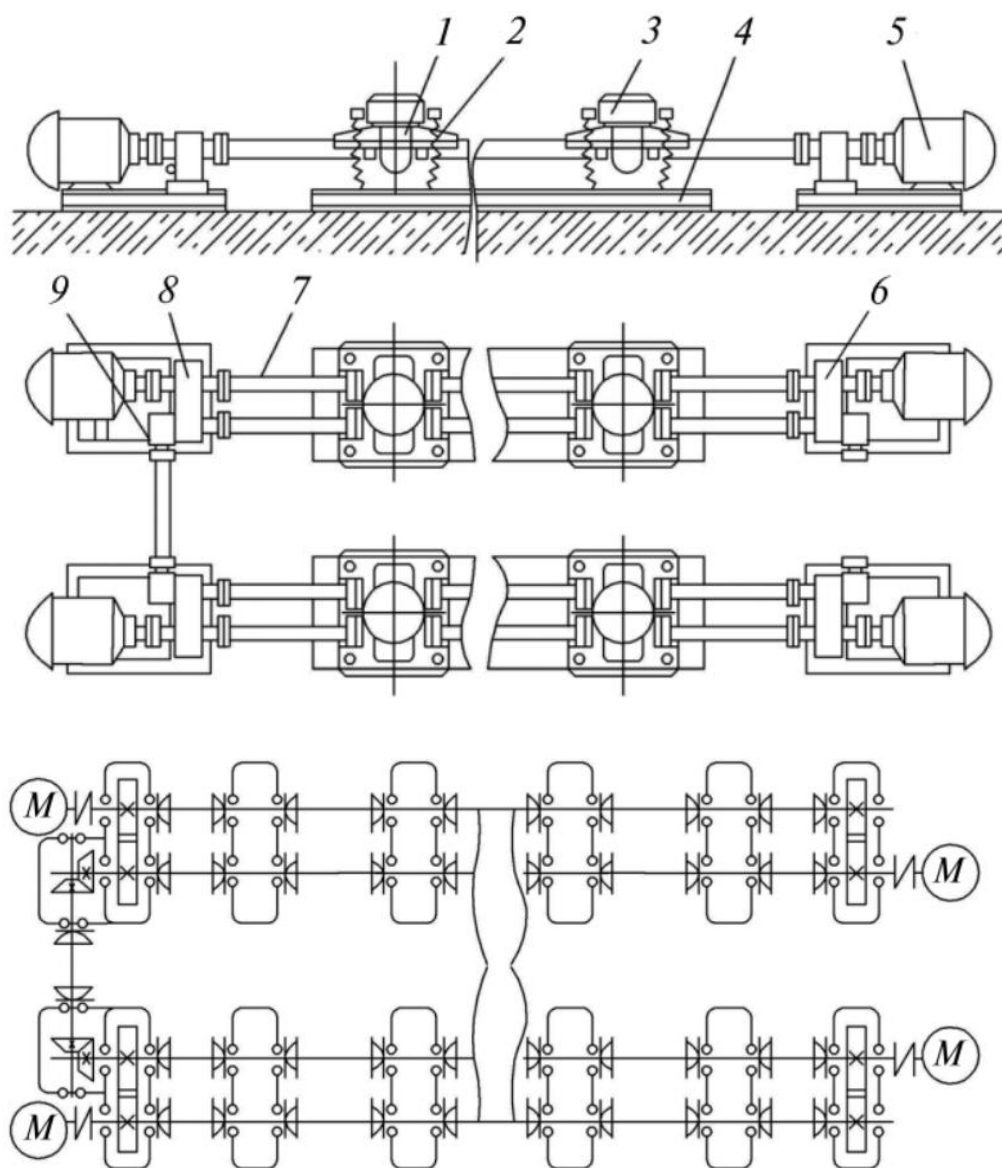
Строительная схема и схема перемещений Виброплощадка СМЖ-187А: 1 — виброблок; 2 — цилиндрические пружины; 3 — электромагнит; 4 — рама; 5 — электродвигатель; 6 — синхронизатор; 7 — карданный вал; 8 — рама привода; 9 — коническая приставка
